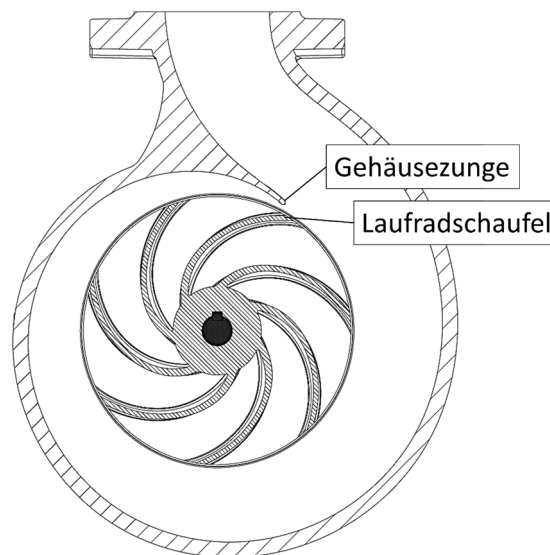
Schnittansicht des Gehäuses und Laufrades von PO001 mit Bezeichnung der Gehäusezunge sowie der Laufradschaufeln.
